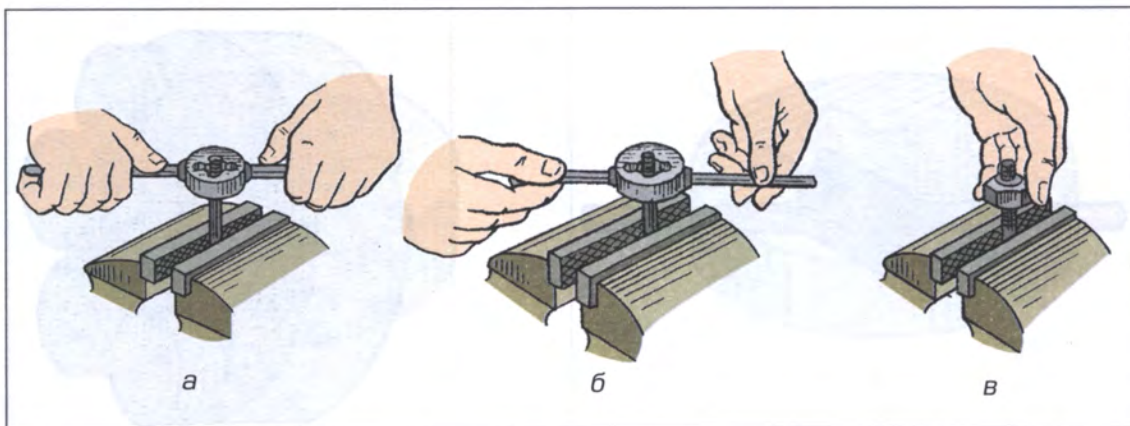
Процесс нарезания резьбы: установка плашки (а), резание (б), контроль качества резьбы (в)
